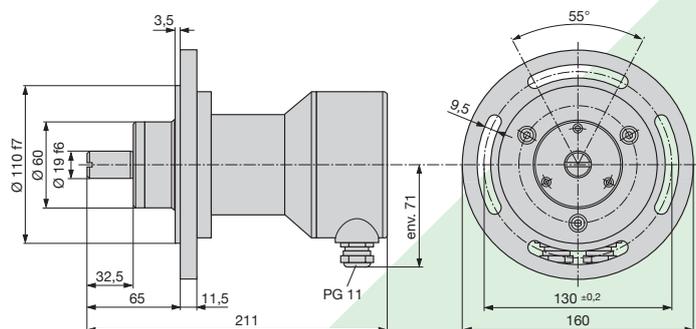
KINAX WT 707 avec engrenage additionnel, bornes à vis, ainsi que presse-étoupes et flasque.
